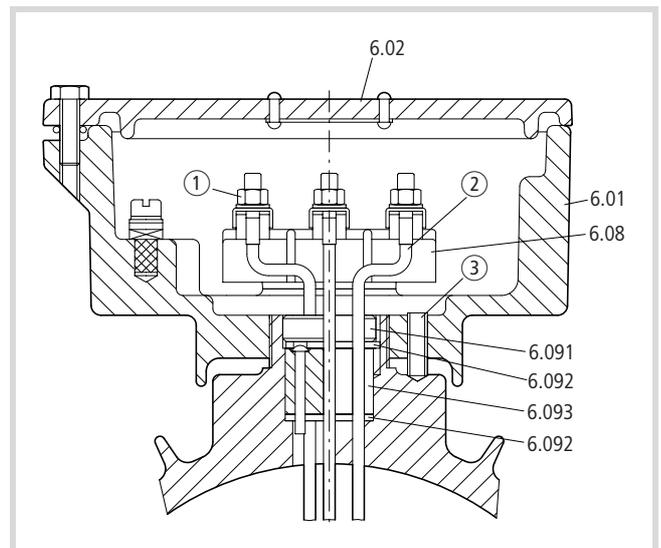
Dévissage des raccordements de la plaque à bornes (6.08)
